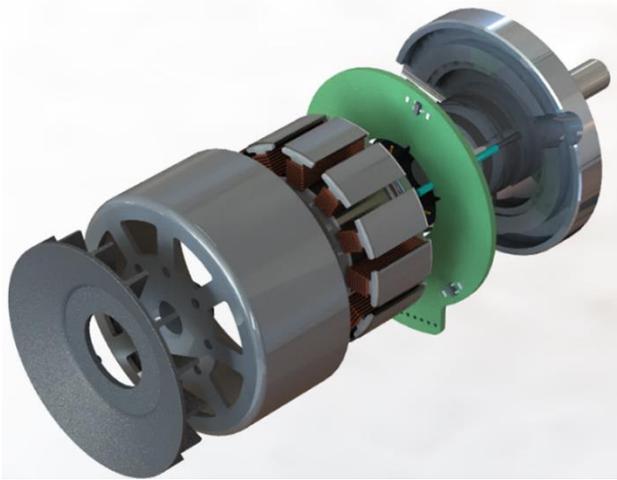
Vue en éclaté d'un moteur à rotor de type à ventilateur intégré.
